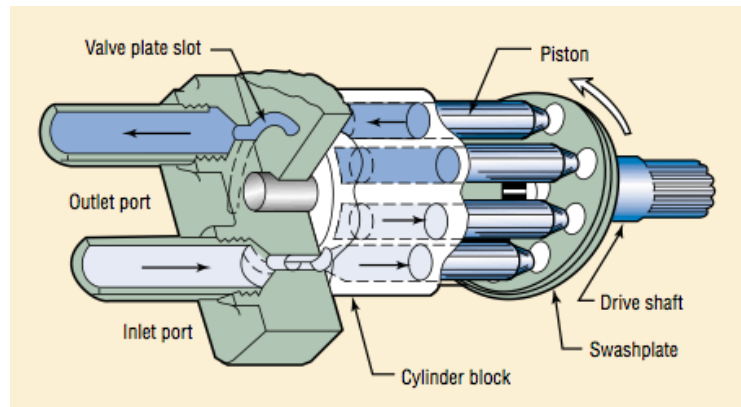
Funcionamiento de Bomba de pistones axiales (Fuente: Bosch Rexroth)
